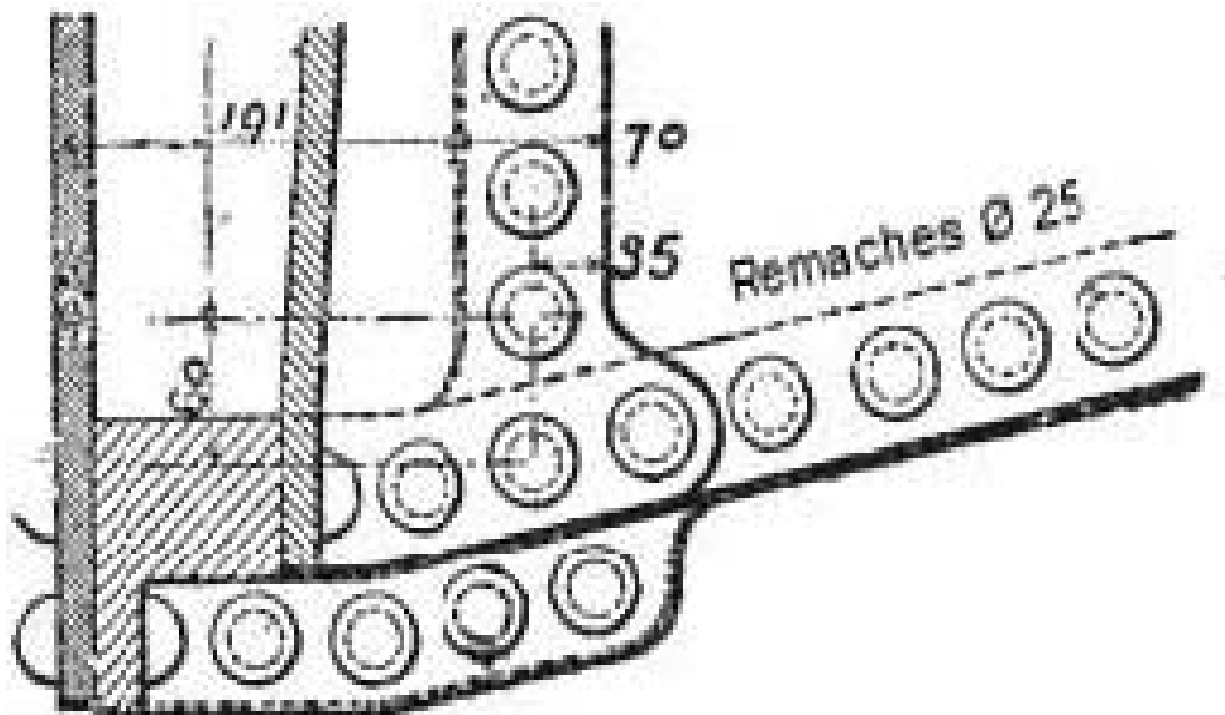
Oreja del marco, sobre la que se remacha la caja de fuego.
